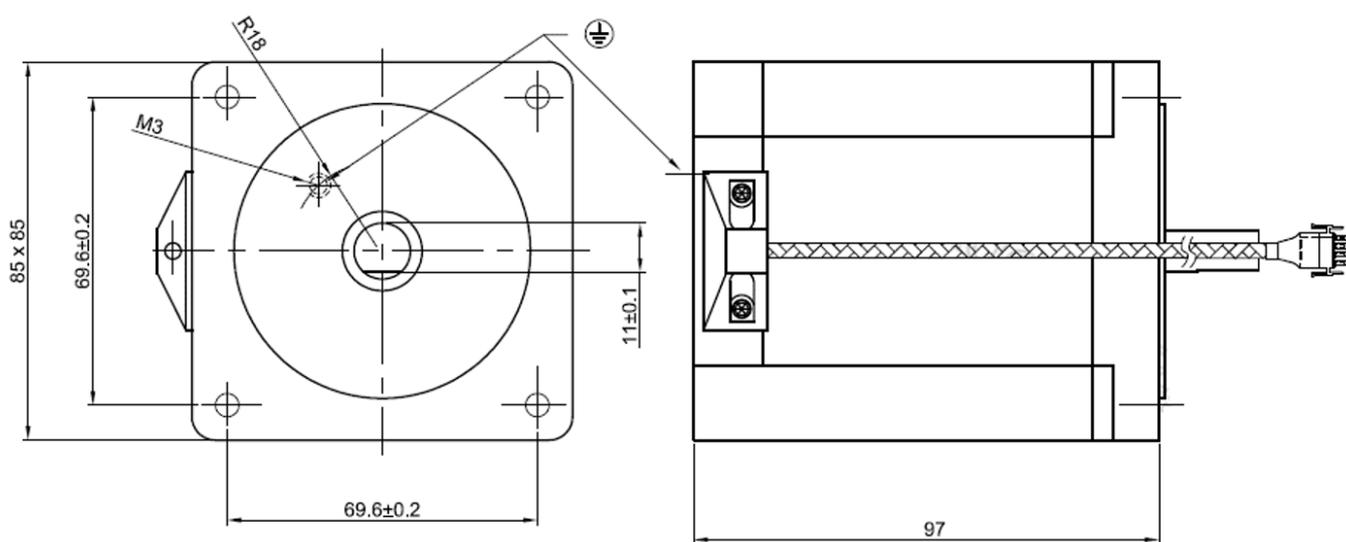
Шаговый двигатель 4 Нм (все размеры указаны в миллиметрах)
